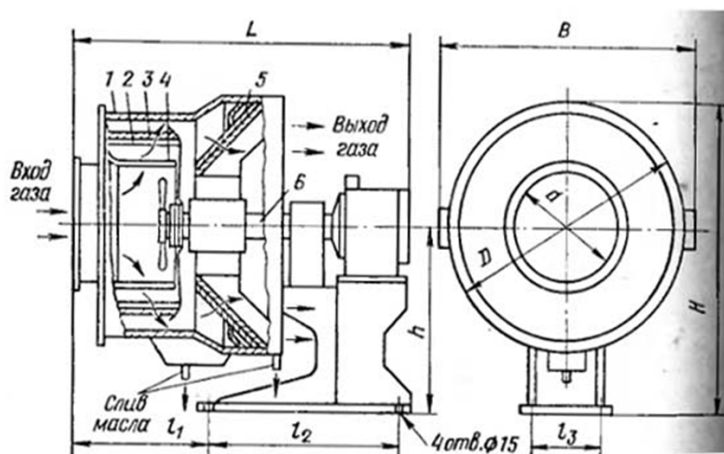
Ротационный фильтр типа ФРМ для улавливания масляного тумана: 1 – корпус; 2 – фильтрующий материал; 3 – перфорированный барабан; 4 – вентиляторное колесо; 5 – брызгоуловитель; 6 – вал³⁰
